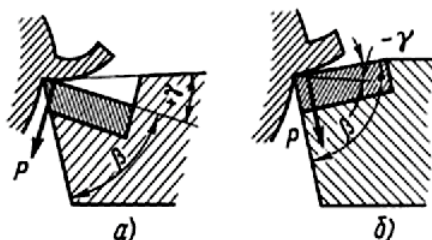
Резец с положительным (а) и отрицательным (б) передним углом
